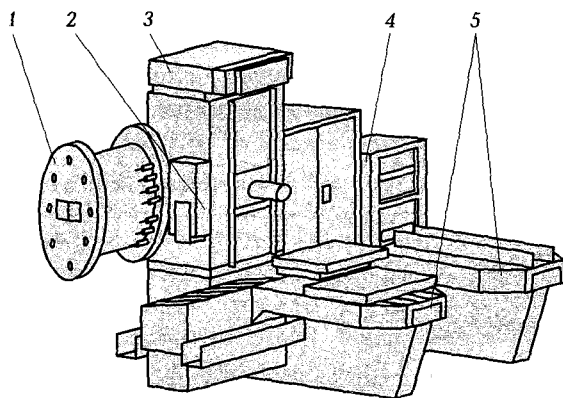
Общий вид и компоновка многоцелевого станка:
